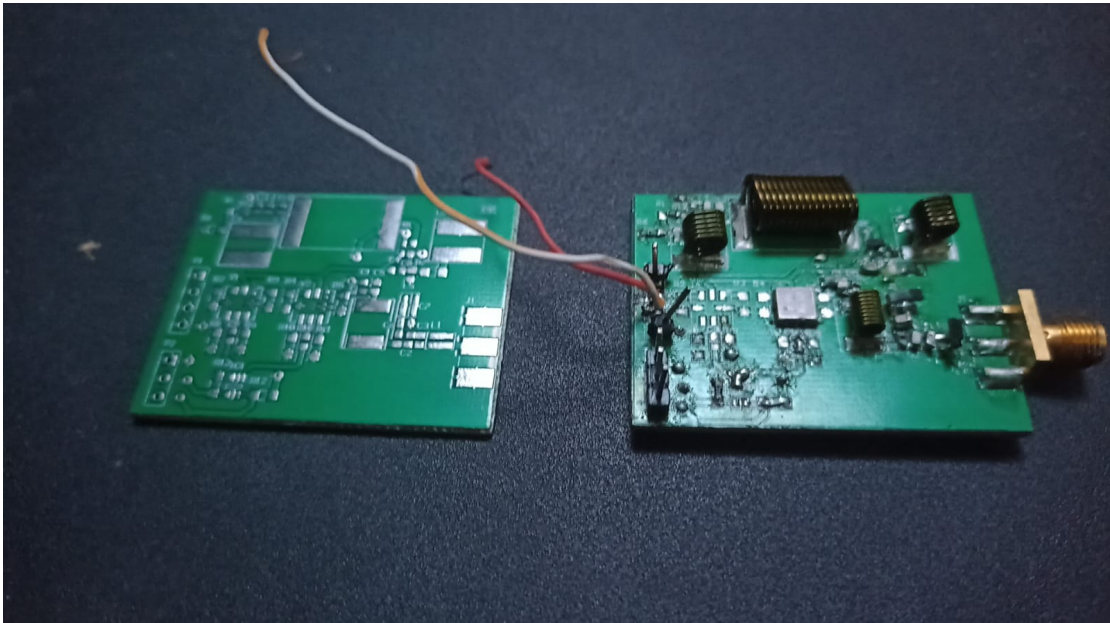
Placa de Circuito Impresso do oscilador Colpitts: sem; e com os componentes eletrônicos soldados na placa.
